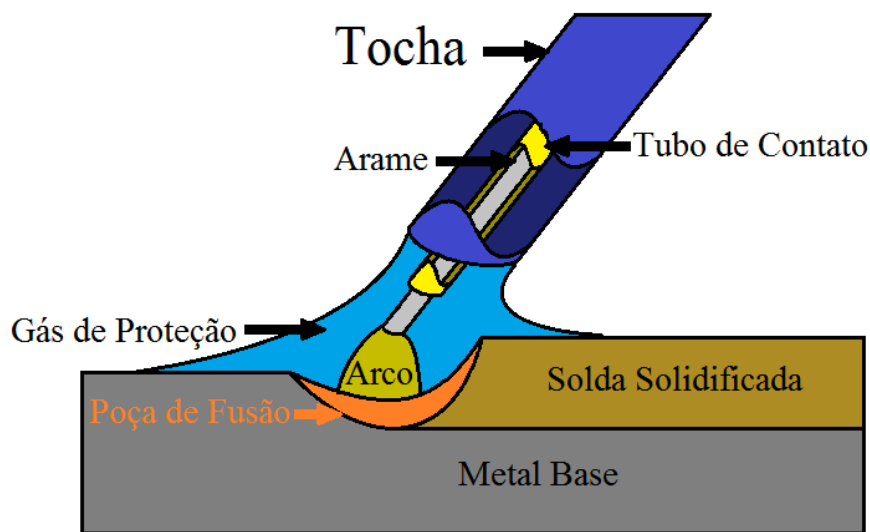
Diagrama: Gas Metal Arc Welding (GMAW)
